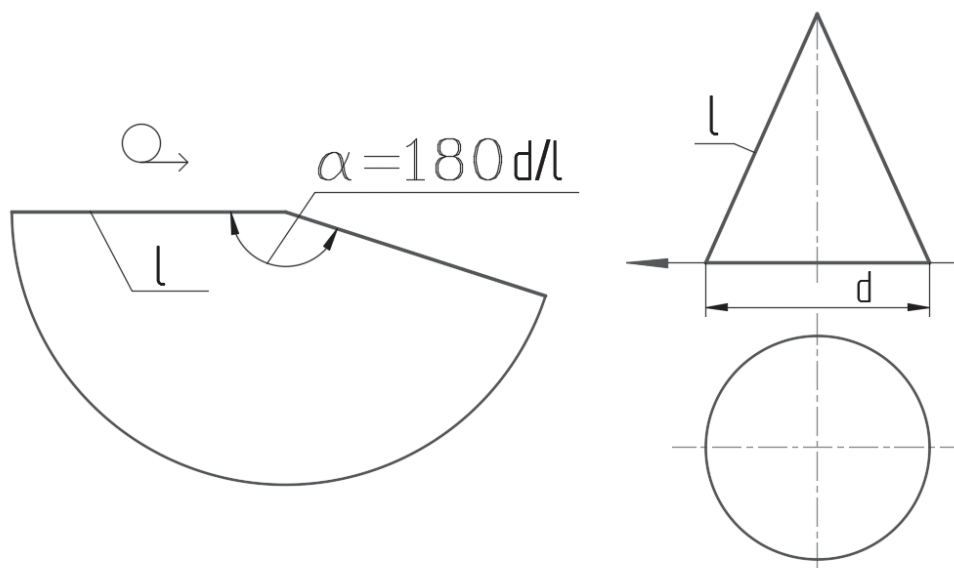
Точная развертка боковой поверхности конуса прямого кругового
